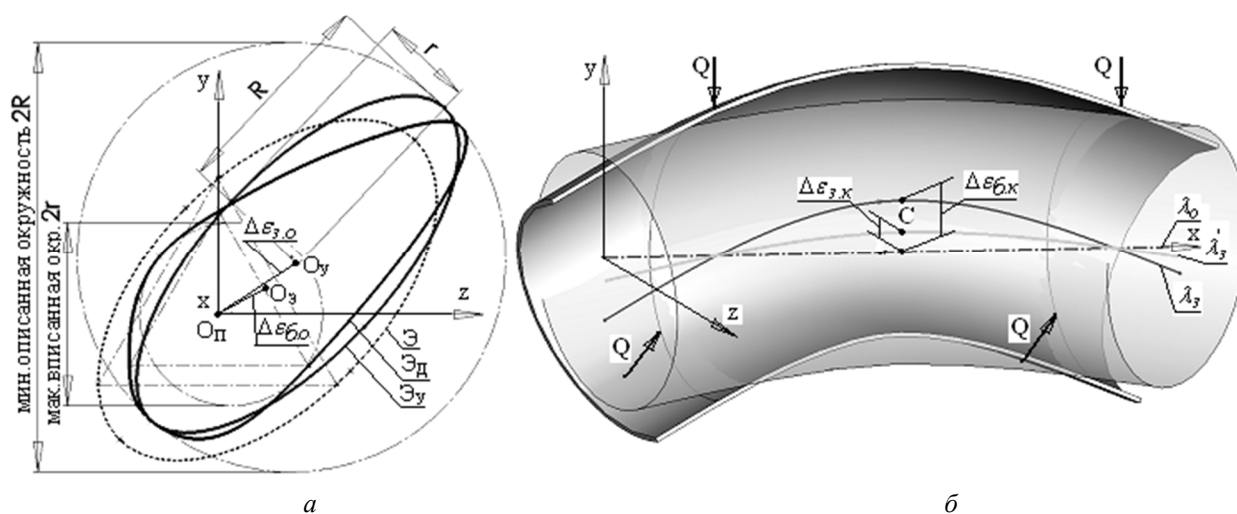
Условный эллипс и погрешности заготовки на стадии закрепления:
